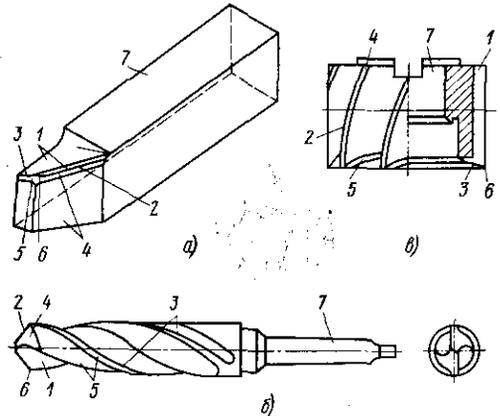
Геометрические и конструктивные элементы режущих инструментов: а — токарного резца; б — сверла; в — фрезы: 1 — передняя поверхность лезвия; 2 — главная режущая кромка; 3 — вспомогательная режущая кромка; 4 — главная задняя поверхность лезвия; 5 — вспомогательная задняя поверхность лезвия; 6 — вершина лезвия; 7 — крепежная часть инструмента
